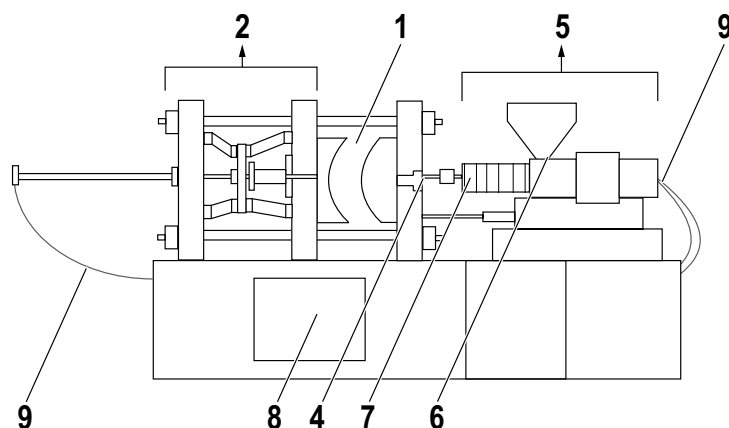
Aree di pericolo della macchina di stampaggio a iniezione (vista frontale)
